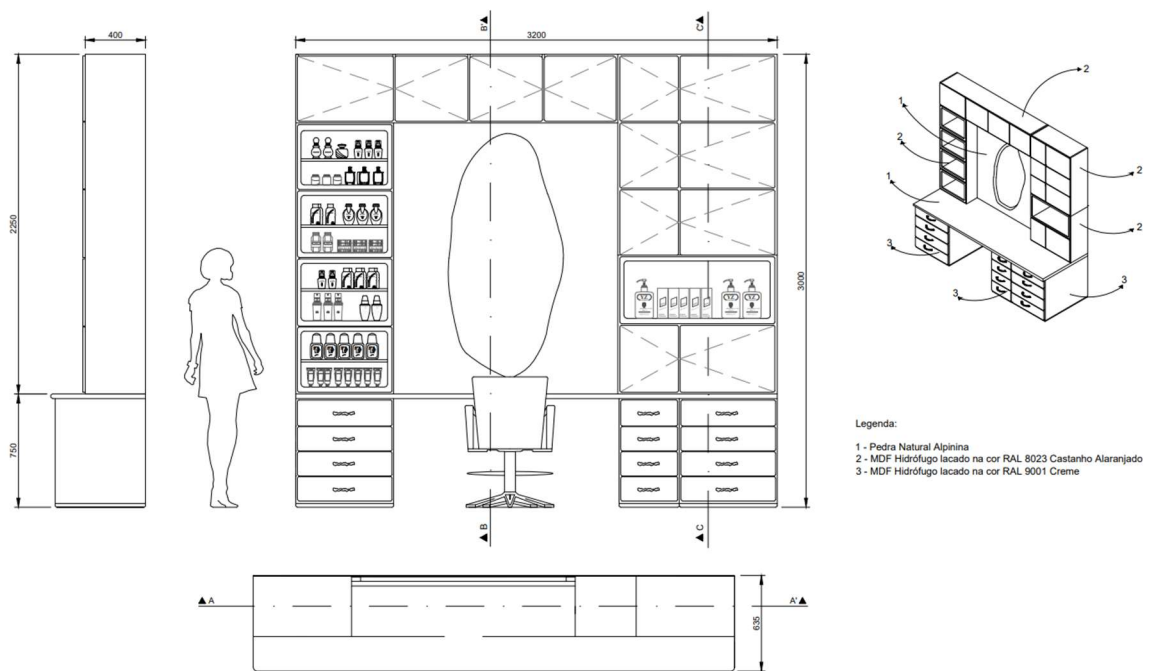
Desenho de Conjunto do Equipamento; Fonte: Autor
